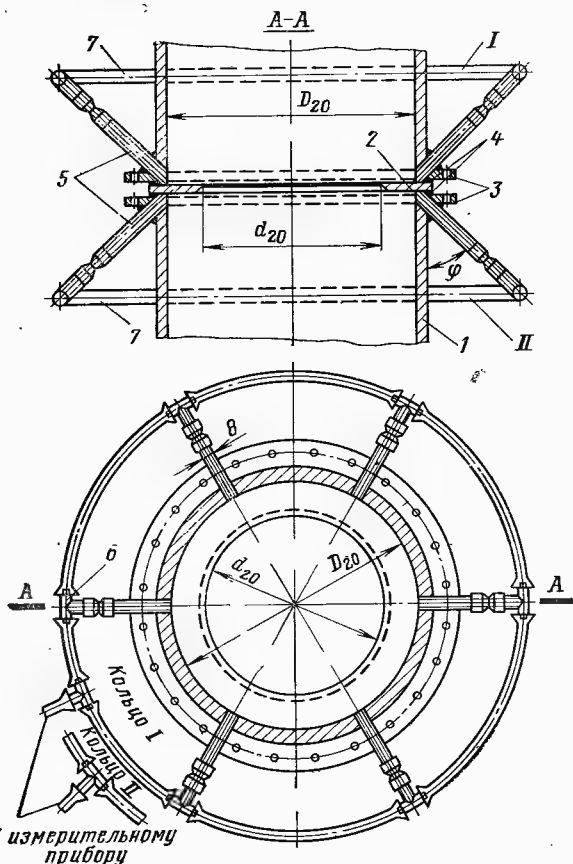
Стандартная диафрагма с трубчатыми кольцевыми камерами.
